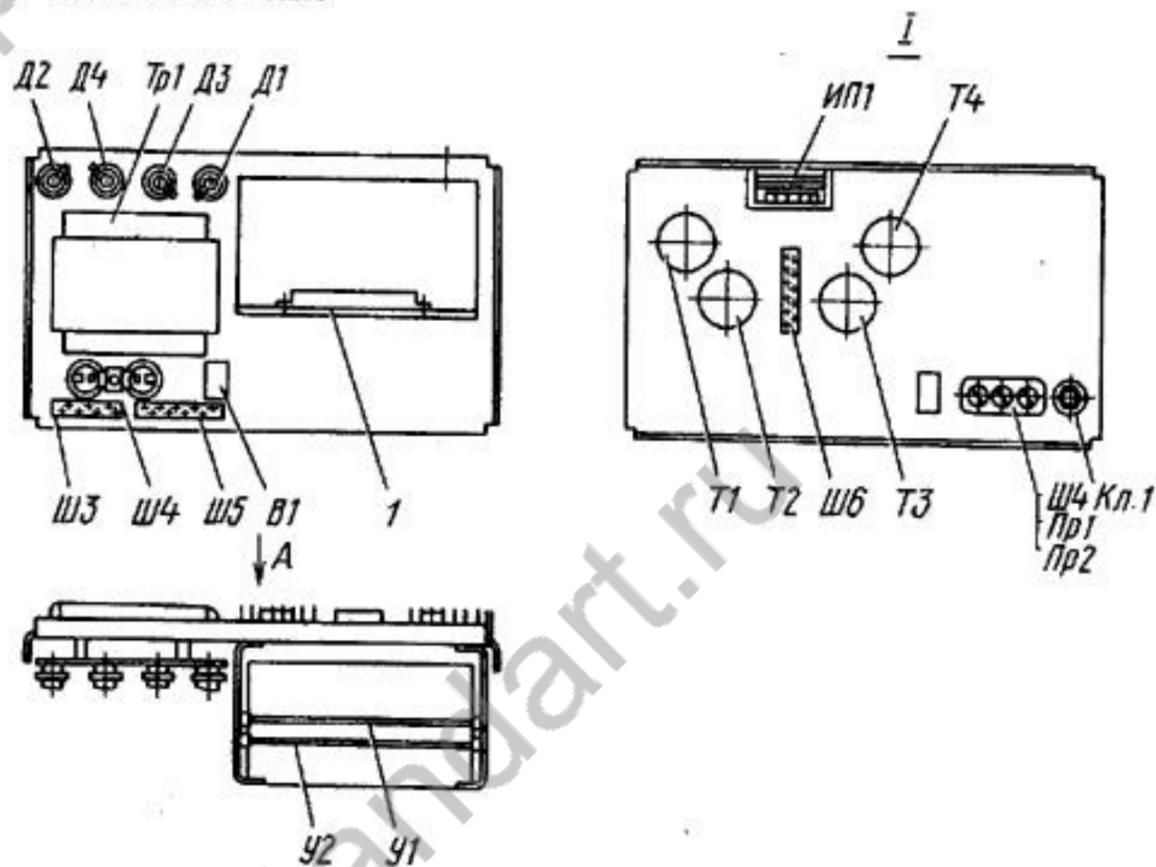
Блок питания 2.087.034. План размещения элементов:
